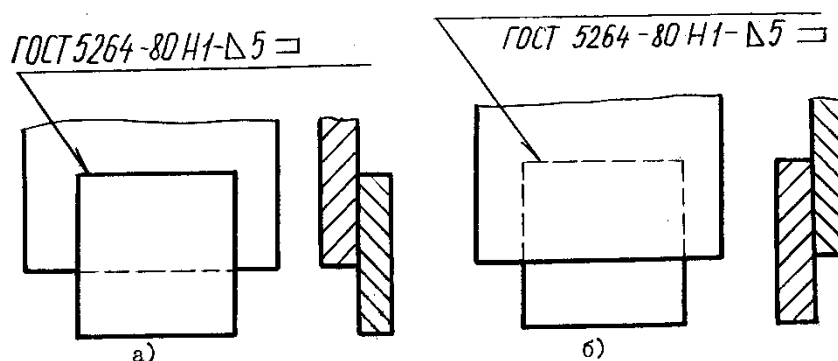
Обозначение видимого и невидимого сварного шва
